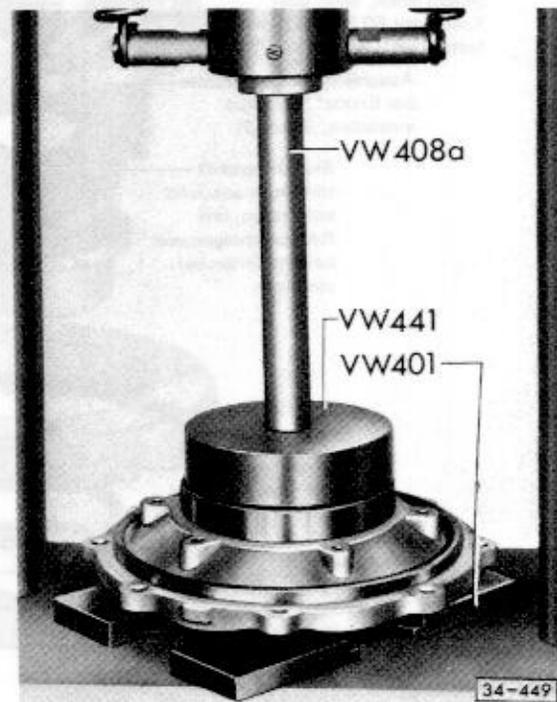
Rillenkugellager für Ausgleichgetriebe einpressen
